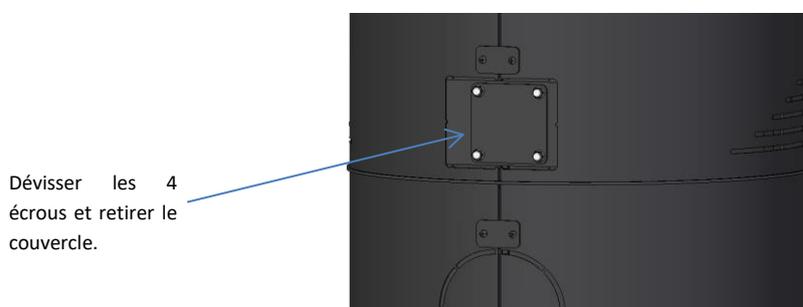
Vue arrière de l'équipement, retirer le couvercle du sas extérieur
